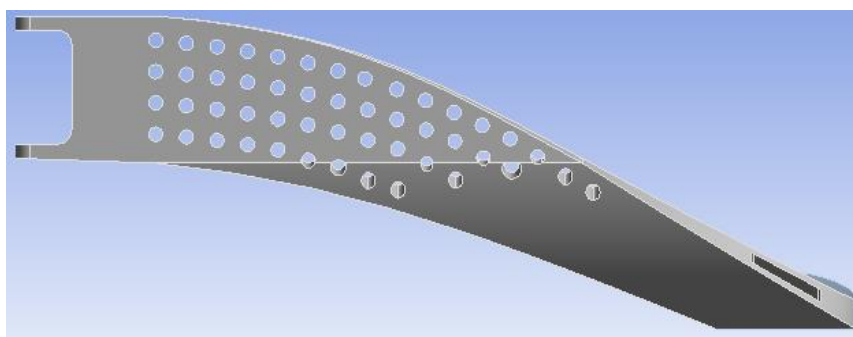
Diseño N°6 eslabón pierna izquierda, vista 3.
